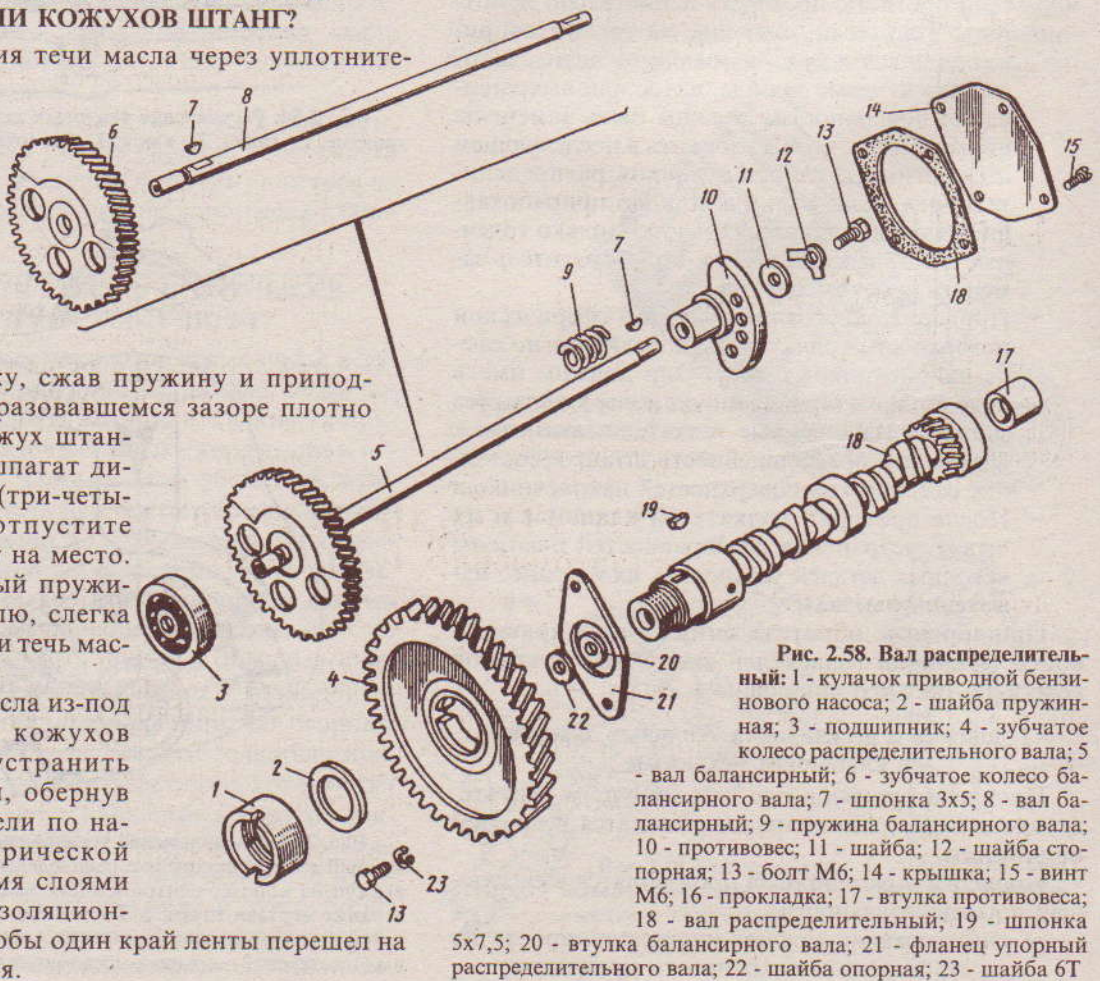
Вал распределительный: 1 – кулачок приводной бензинового насоса; 2 – шайба пружинная; 3 – подшипник; 4 – зубчатое колесо распределительного вала; 5 – вал балансирный; 6 – зубчатое колесо балансирного вала; 7 – шпонка 3x5; 8 – вал балансирный; 9 – пружина балансирного вала; 10 – противовес; 11 – шайба; 12 – шайба стопорная; 13 – болт М6; 14 – крышка; 15 – винт М6; 16 – прокладка; 17 – втулка противовеса; 18 – вал распределительный; 19 – шпонка 5x7,5; 20 – втулка балансирного вала; 21 – фланец упорный распределительного вала; 22 – шайба опорная; 23 – шайба 6Т
